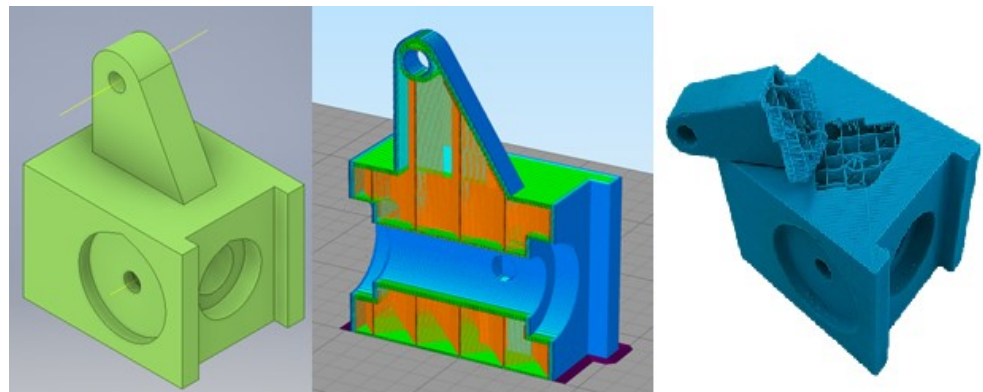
Модель детали «кулак», разрез симуляции детали со стандартными настройками печати и реальная деталь
